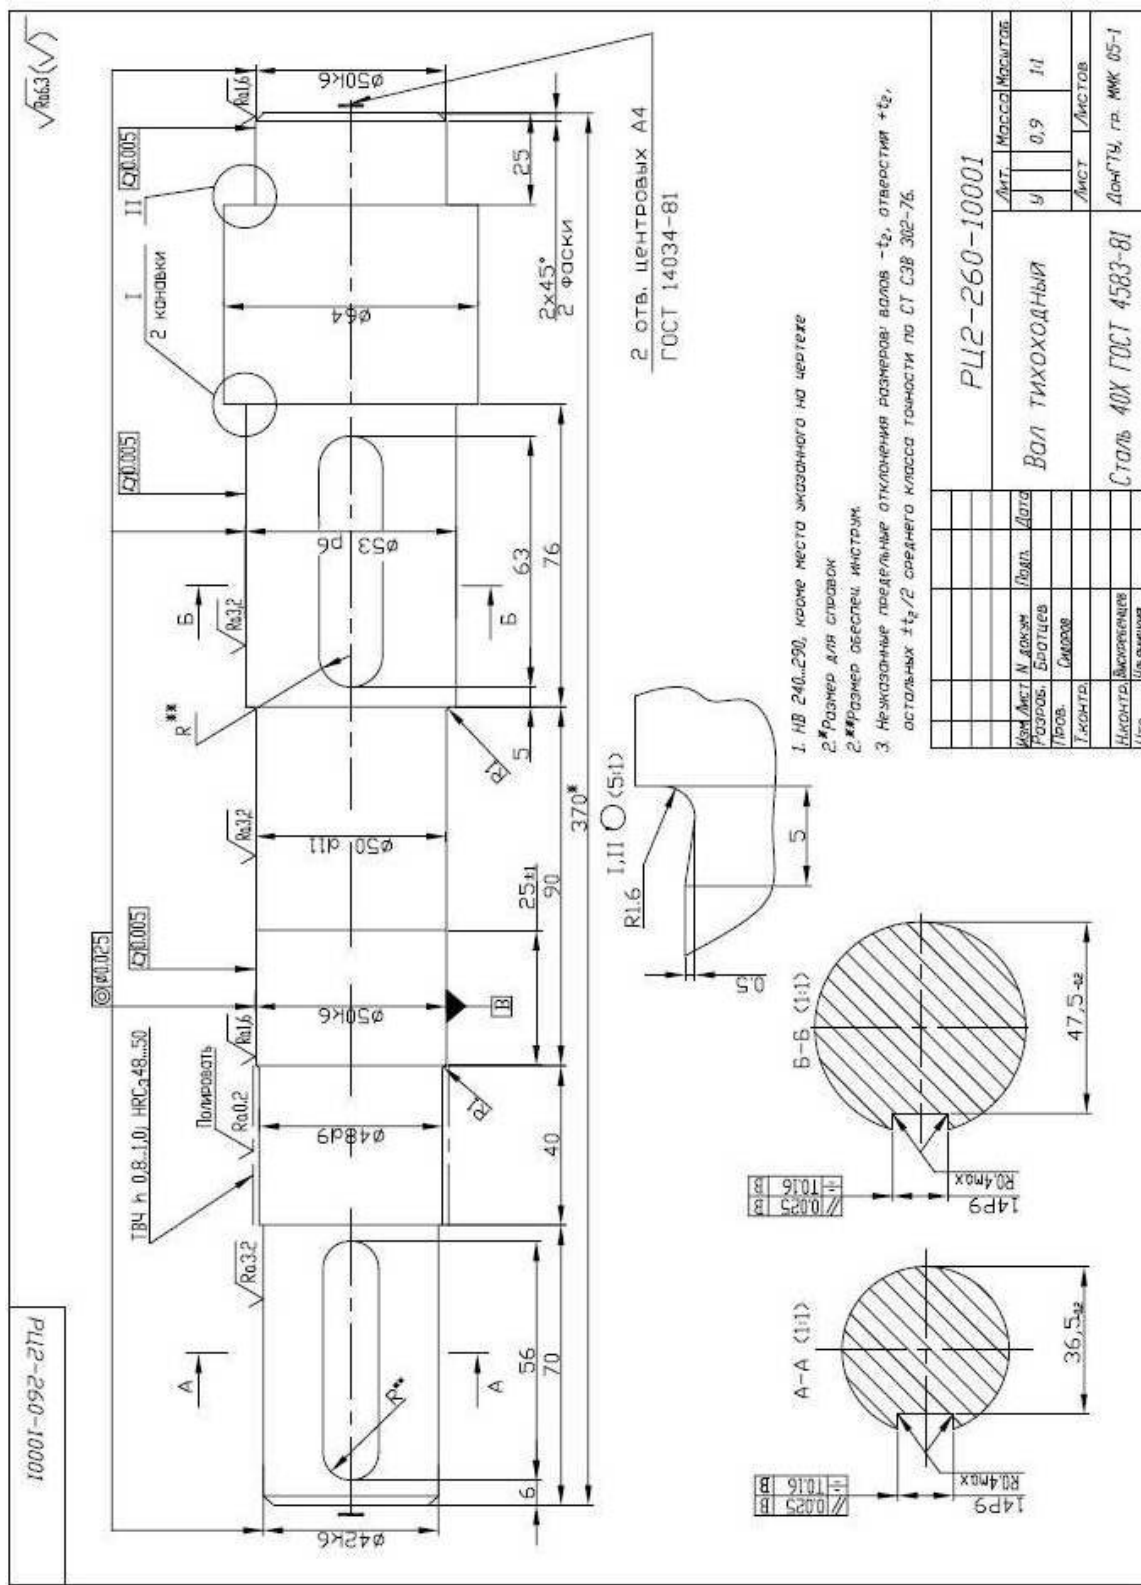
Укрупненный вид детализовки вала редуктора на рисунке К.6
